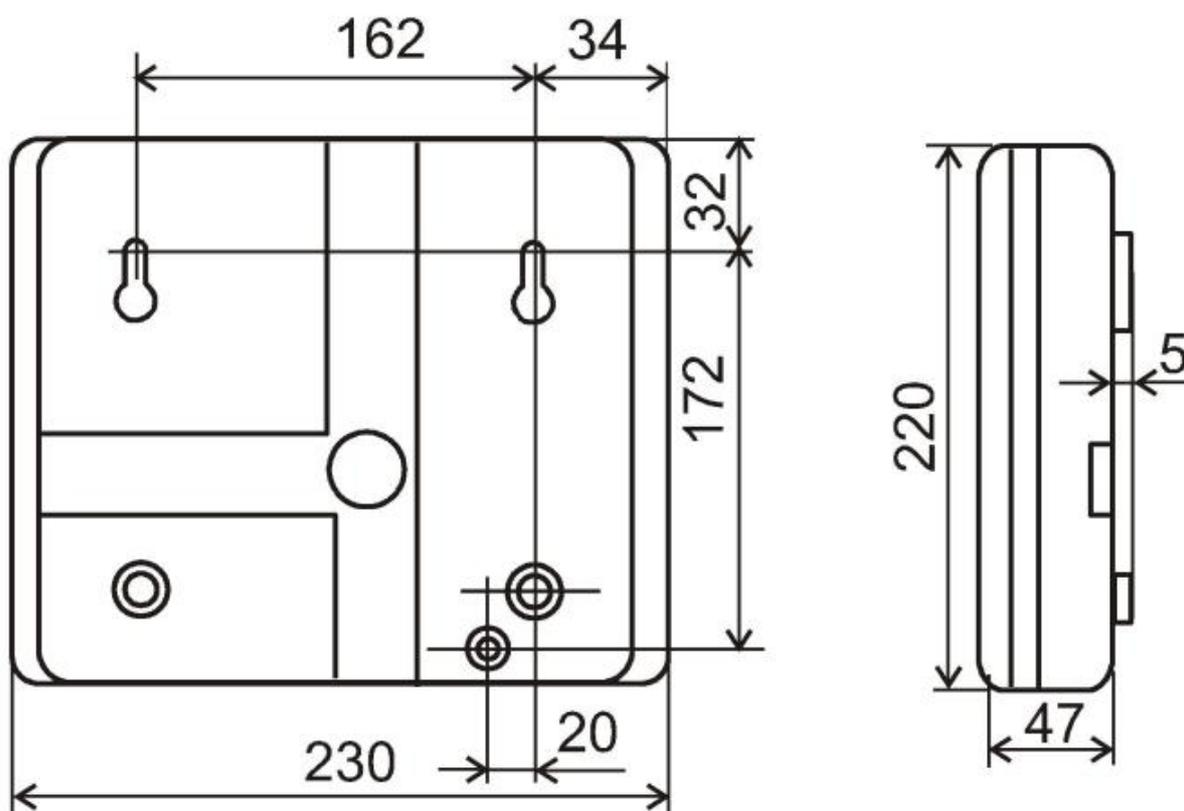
б. Габаритные и установочные размеры устройства.
